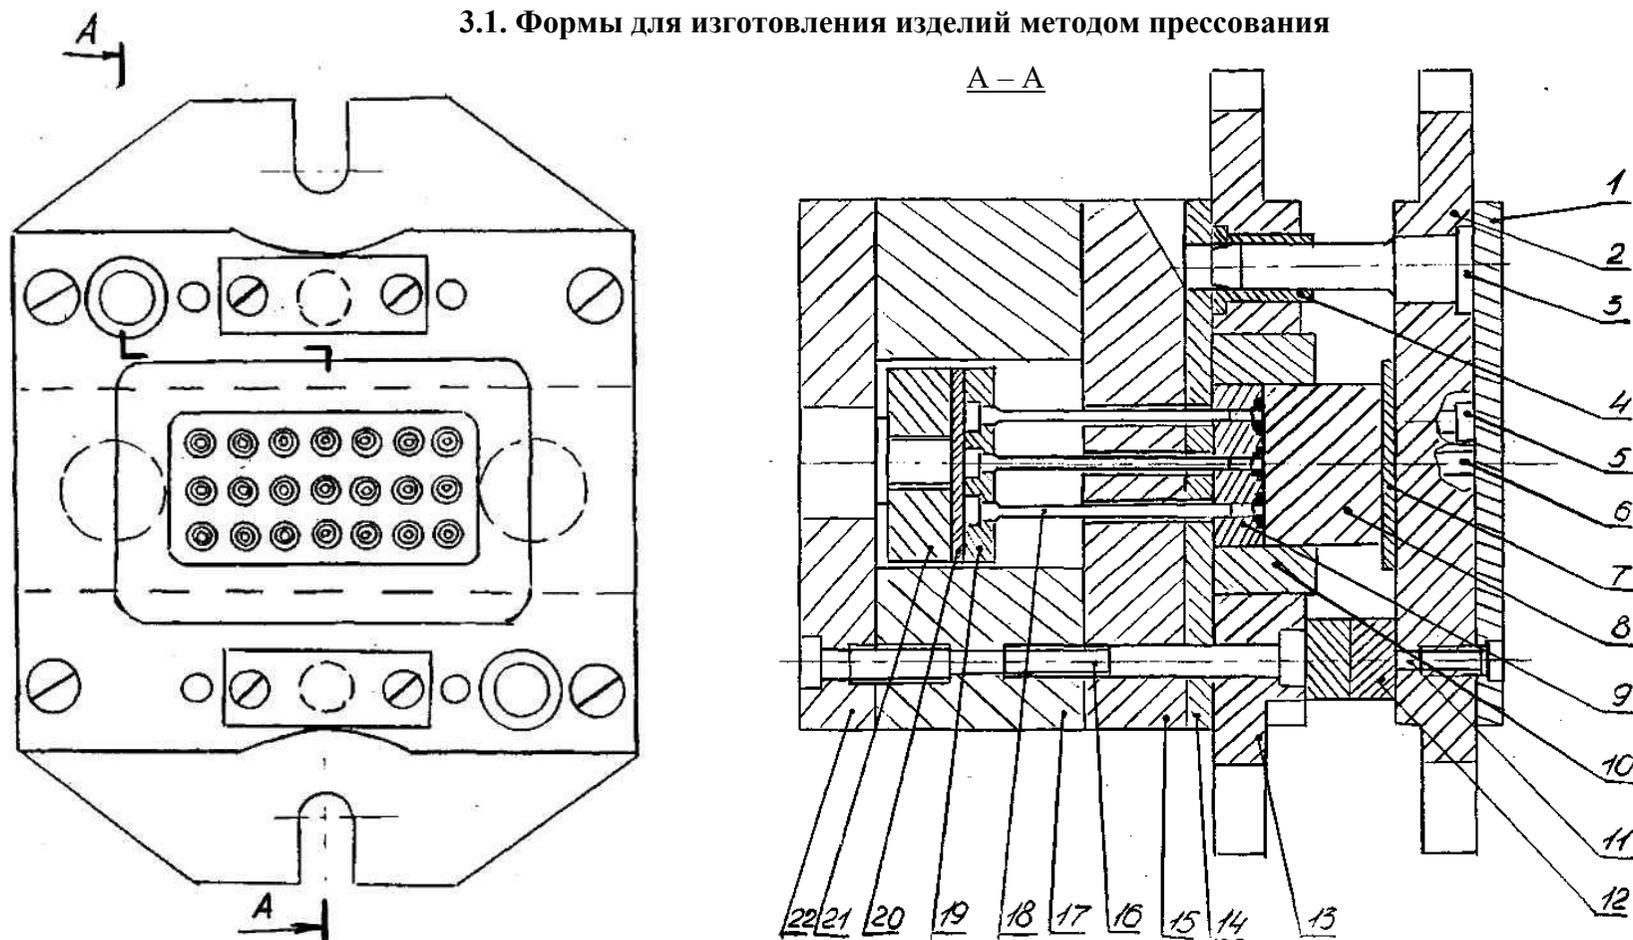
Пресс-форма для изготовления деталей методом прессования:
